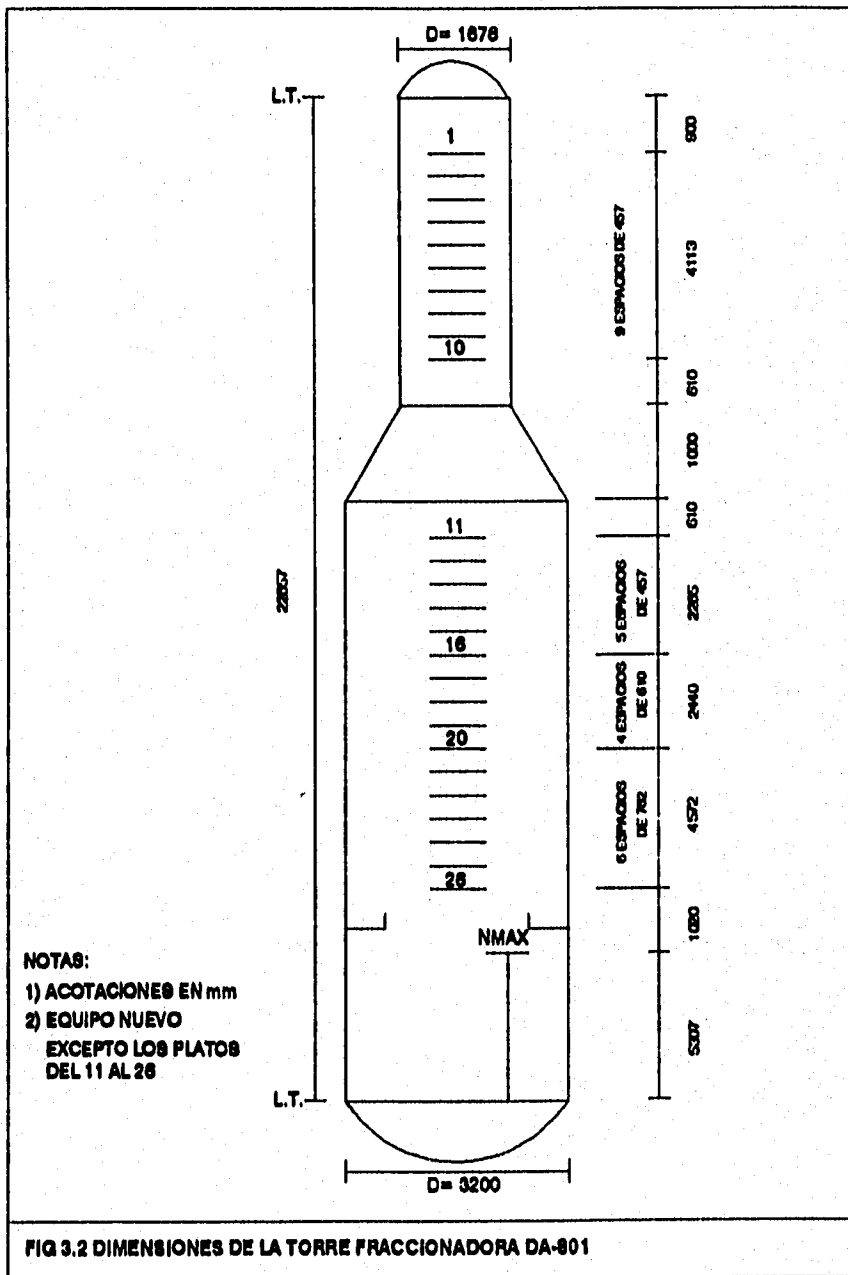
DIMENSIONES DE LA TORRE FRACCIONADORA DA-801
